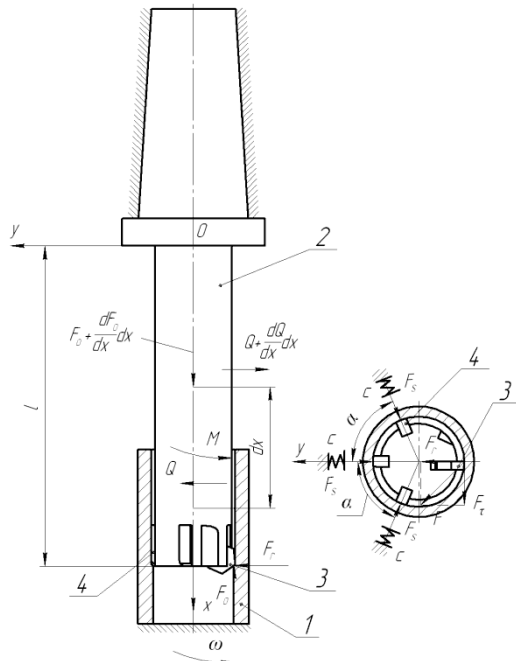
Розрахункова схема для дослідження деформації розточної оправки із напрямними опорами: 1 – заготовка; 2 – оправка; 3 – ріжуча пластина; 4 – напрямна опора
